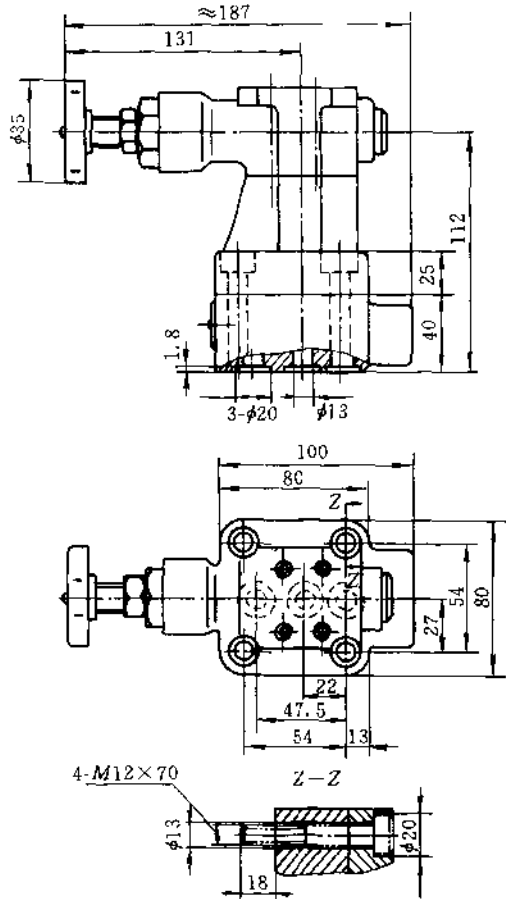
HY-H*10 型卸荷溢流阀外形尺寸图
